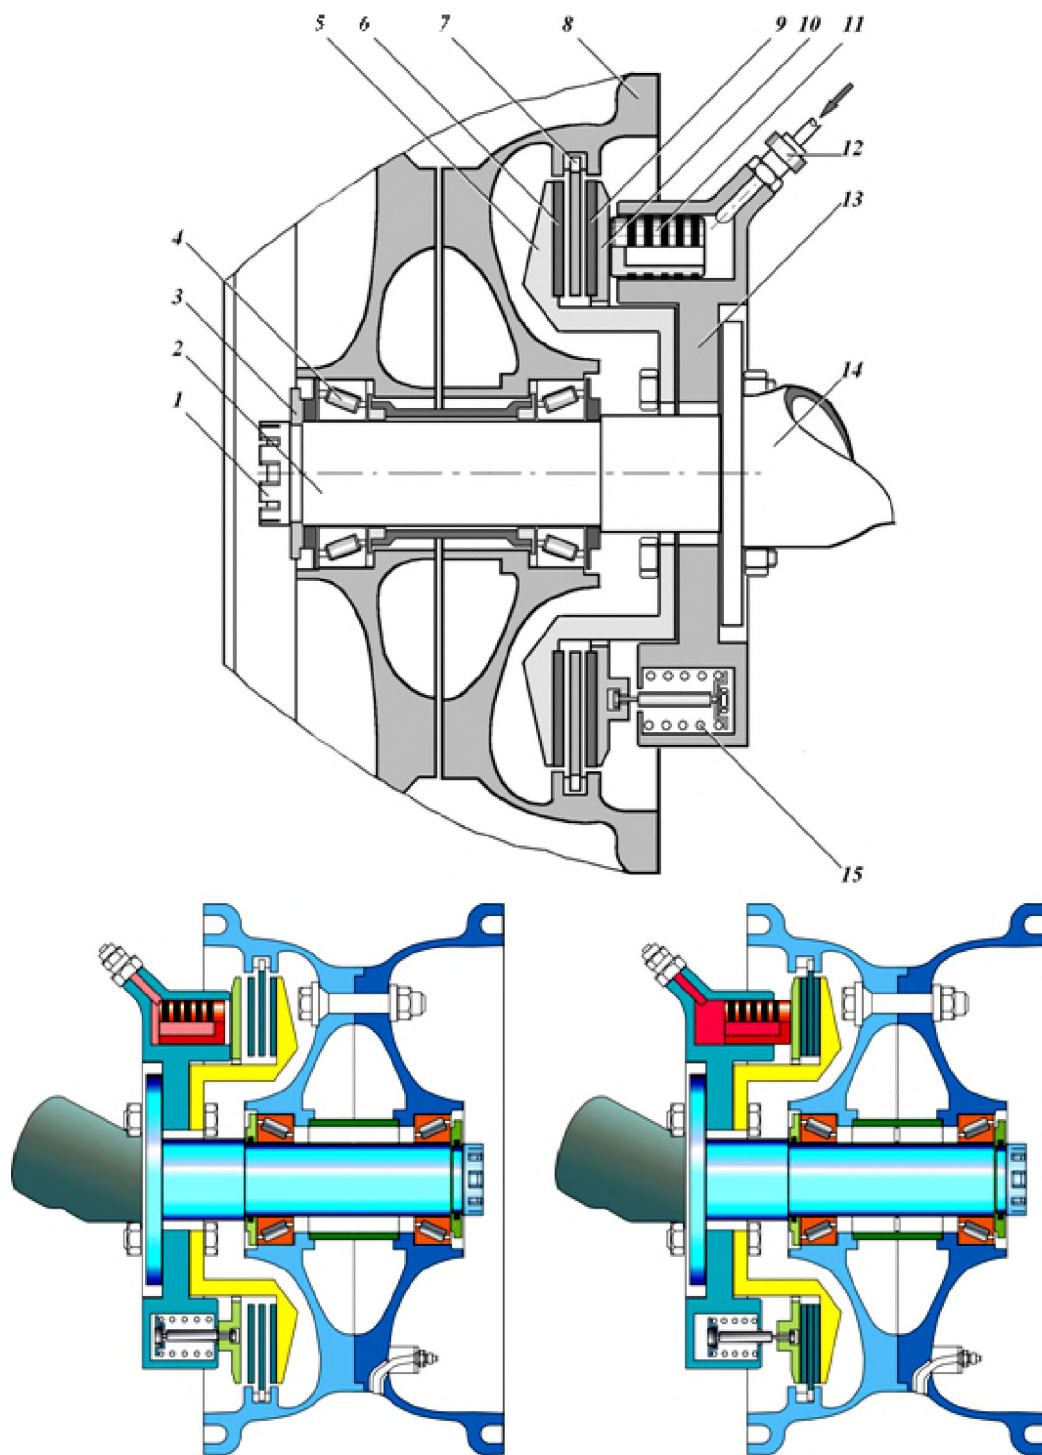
Конструкция и работа тормоза колеса основной опоры шасси вертолета "АНСАТ-У" [9]: 1 – гайка; 2 – ось колеса; 3 – шайба; 4 – роликовый подшипник; 5 – неподвижный тормозной диск; 6, 9 – тормозная колодка; 7 – диск колеса; 8 – барабан колеса; 10 – нажимной диск; 11 – поршень – толкатель; 12 – штуцер подвода рабочей жидкости к тормозным цилиндрам; 13 – корпус тормоза колеса; 14 – наконечник рычага; 15 – возвратная пружина.
